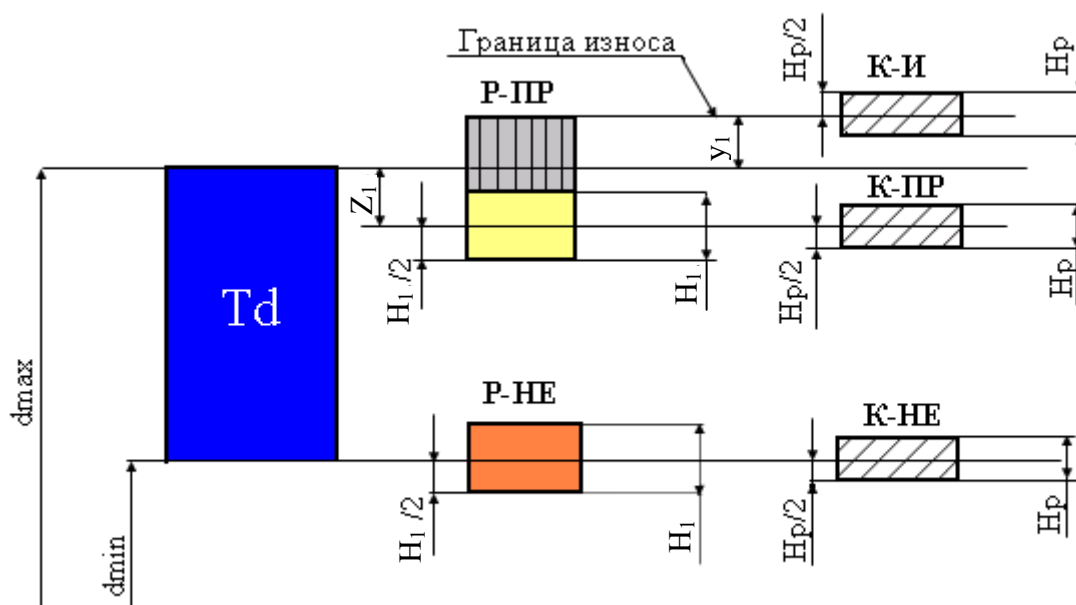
Схема расположения полей допусков калибров для валов IT6-IT8
